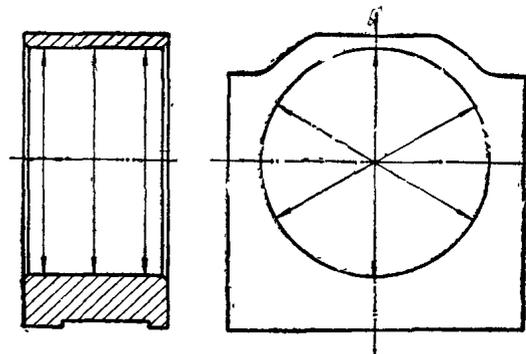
Схема измерения обычных посадочных мест в корпусах подшипников
